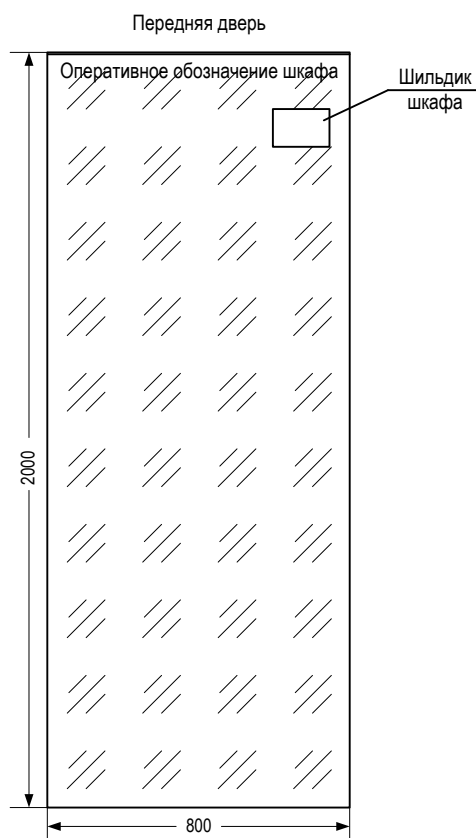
Общий вид обзорной двери типового шкафа
